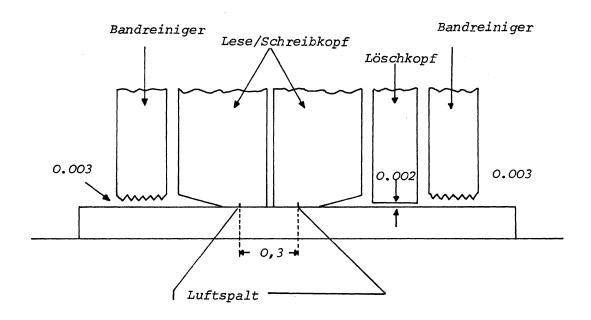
Magnetkopfbaugruppe, Schemazeichnung
